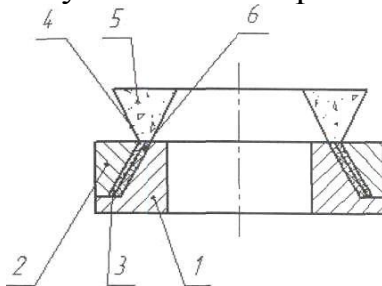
Схема плакування ущільнювального кільця композиційним металом: 1 – керамічна або металева форма; 2 – сталеве кільце, що наплавляється; 3 – порошок наповнювача в зазорі; 4 – живильник із металом матриці; 5 – метал матриці; 6 – не змочуваний розплавом захисний шар на формі
